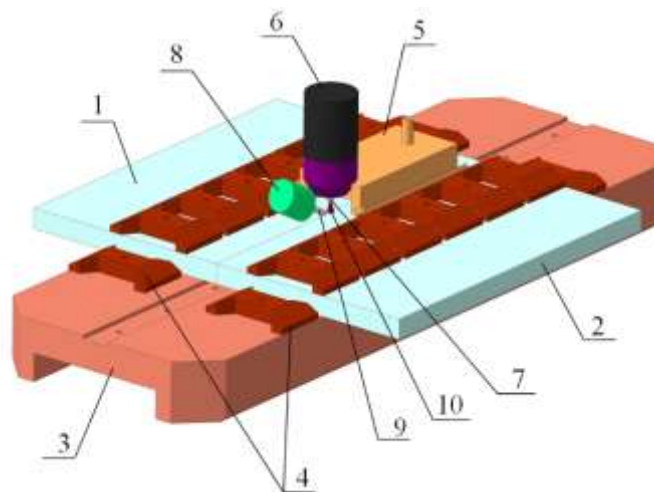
Схематичное изображение процесса автоматической аргонодуговой сварки неплавящимся электродом
